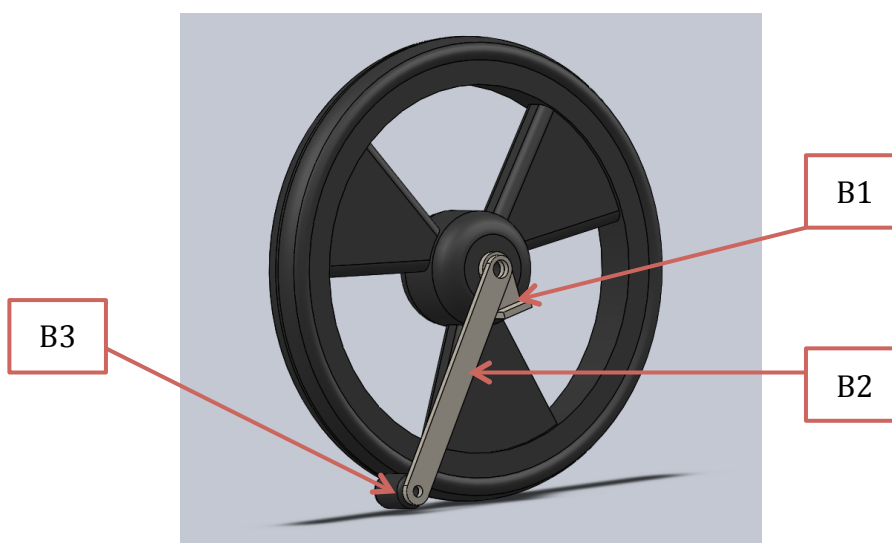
Ubicació del conjunt de peces que formen el sistema de bloqueig de la roda.
